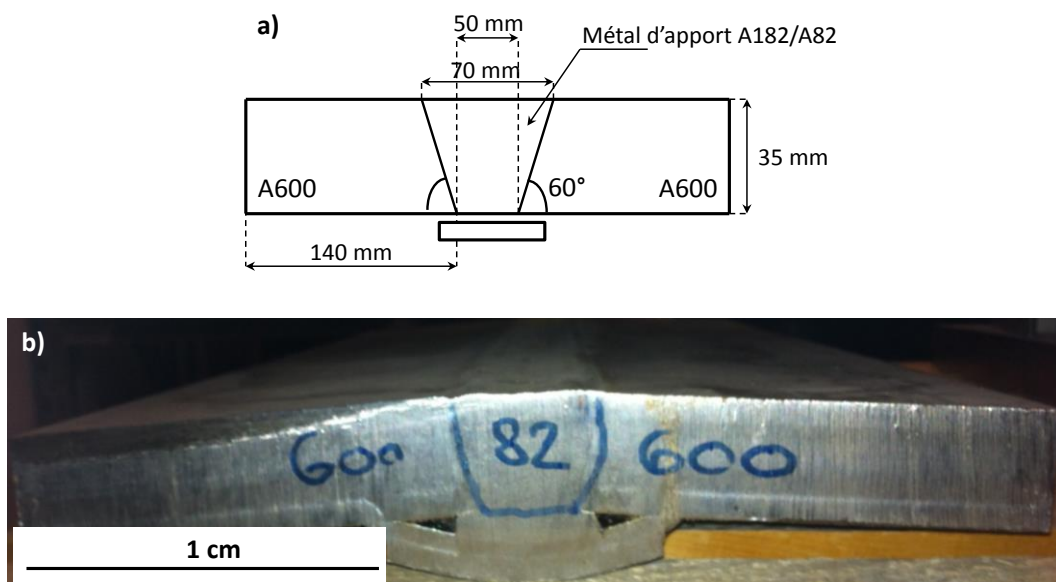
Coupe dans le plan TS d’une soudure (a) représentation schématique avec indication des dimensions (en mm) et (b) image du moule D1072 étudié
